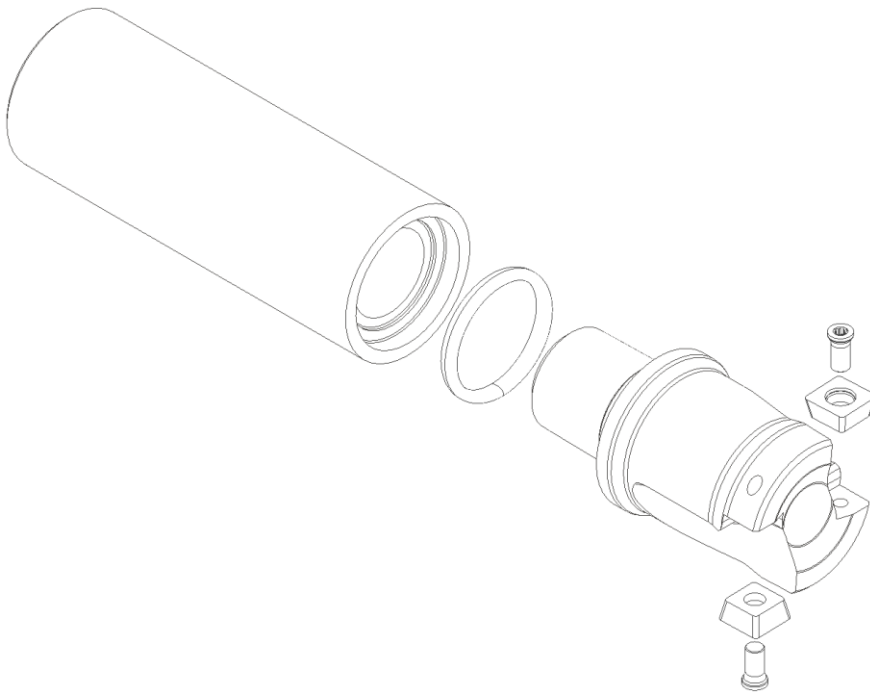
Конструкції збірної кінцевої фрези
